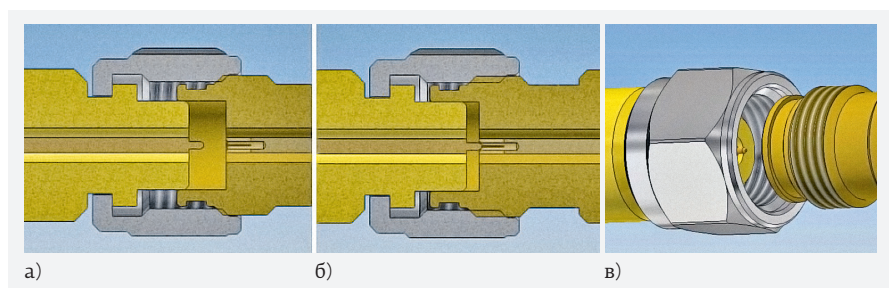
Схема соединения вилки и розетки соединителя 1.35 mm: а – наружных проводников, б – внутренних проводников, в – 3D-вид соединения
